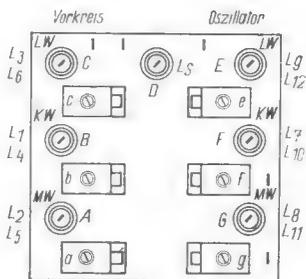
Anordnung der Trimmer und Schraubkerne auf der Spulenplatte
